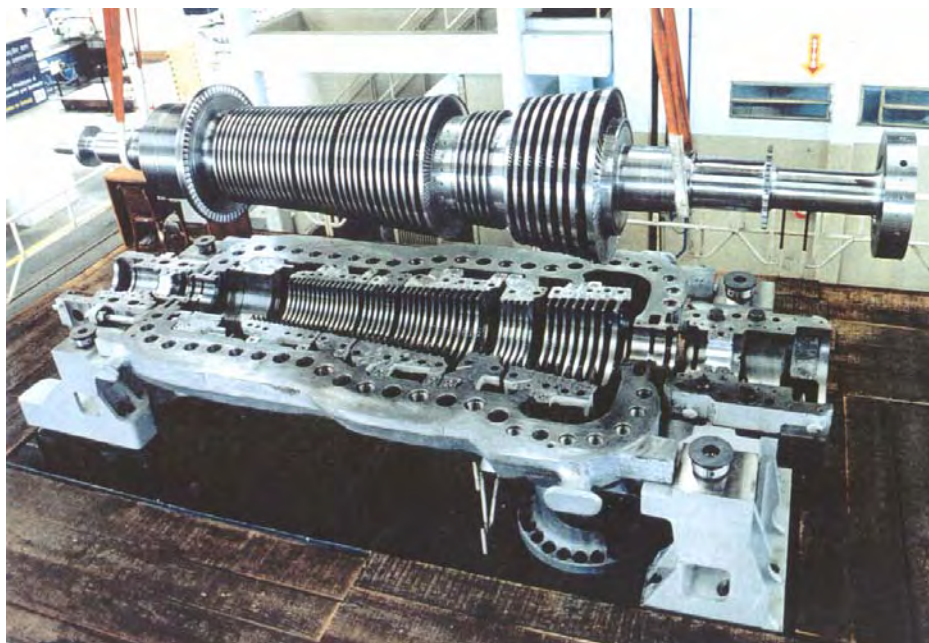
Turbina a vapor multi-estágio - vista do rotor
